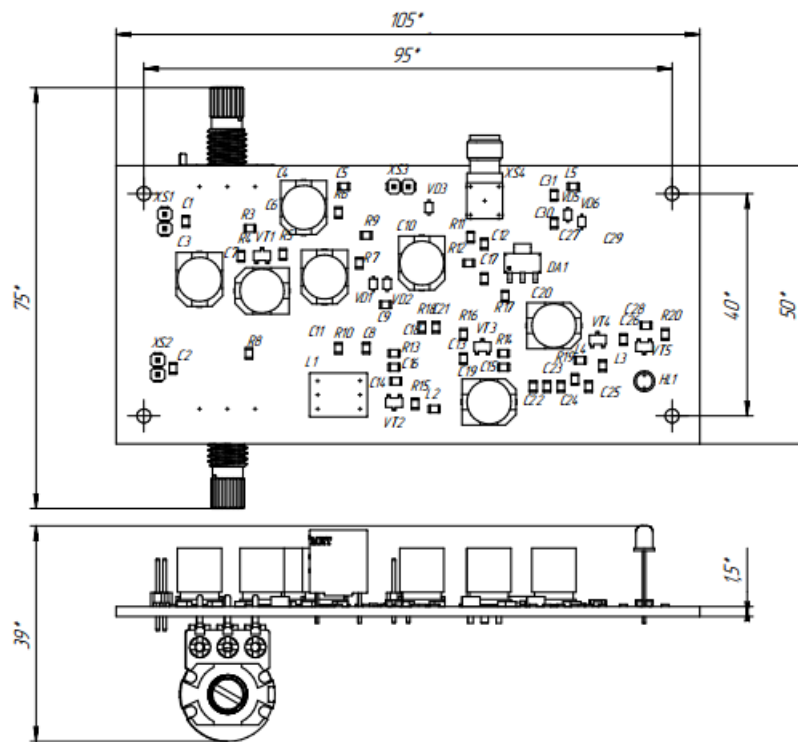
Складальне креслення друкованого вузла (компоновка елементів)
